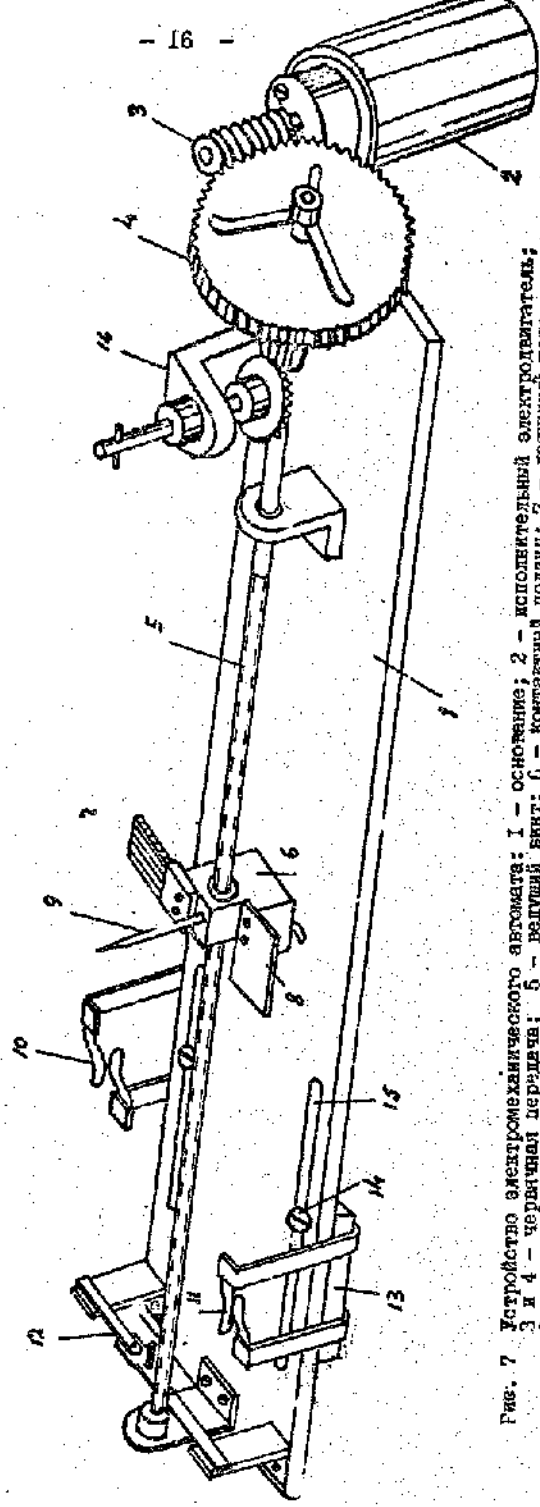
Устройство электромеханического автомата: 1 - основание; 2 - исполнительный электродвигатель; 3 и 4 - червячная передача; 5 - воздушный выкат; 6 - контактная полушка; 7 - контактный нож; 8 - нож из диэлектрика; 9 - шпатель для указания места поворота полушки; 10 - воздушный нож; 11 и 12 - пластины для замыкания контактов; 13 - пластина из диэлектрика; 14 - В и Г; 15 - прорези; 16 - механизм возврата.
